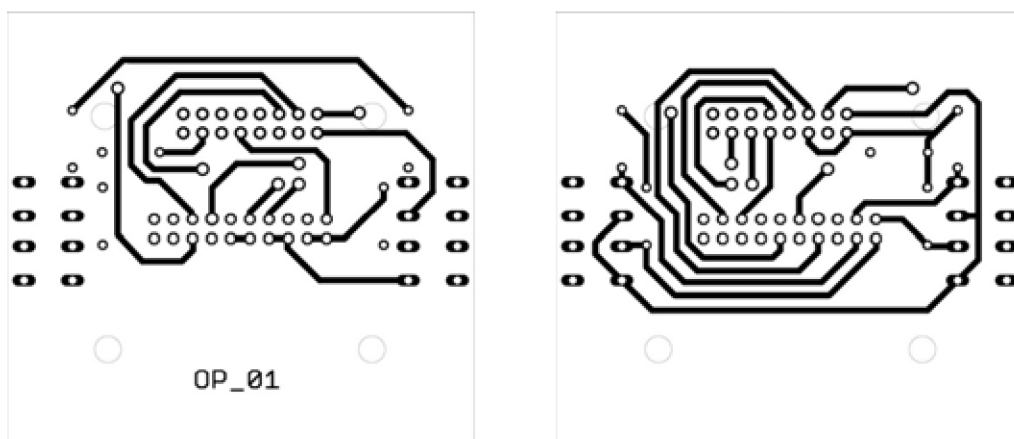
DPS řídicí jednotky – TOP a BOTTOM
